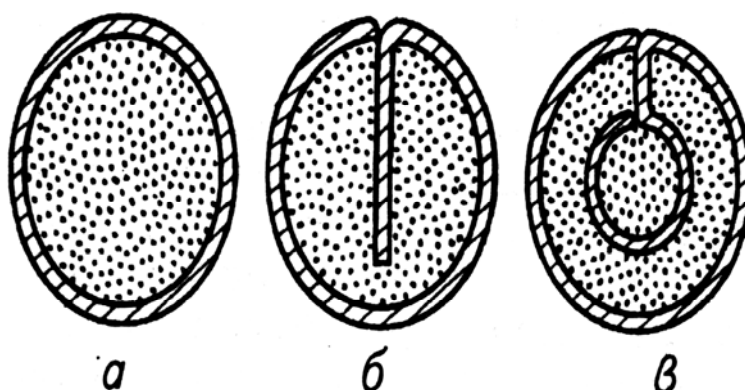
Варианты конструкции сварочной порошковой проволоки по сечению:
